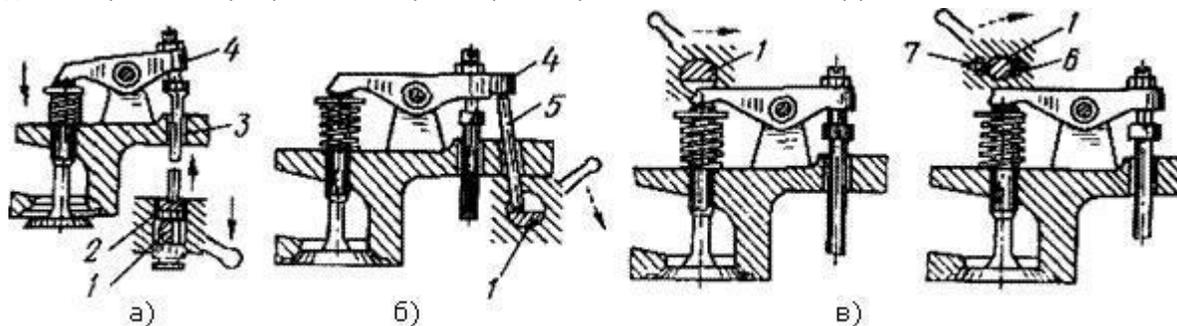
Схеми декомпресійних механізмів: а - з дією валика на штовхач; б - з дією валика через штангу на коротке плече коромисла; в - з натисканням на довше плече коромисла: 1 - валик; 2 - штовхач; 3 - штанга; 4 - коромисло; 5 - штанга декомпресійного механізму; 6 - регулювальний гвинт; 7 - контргайка.
